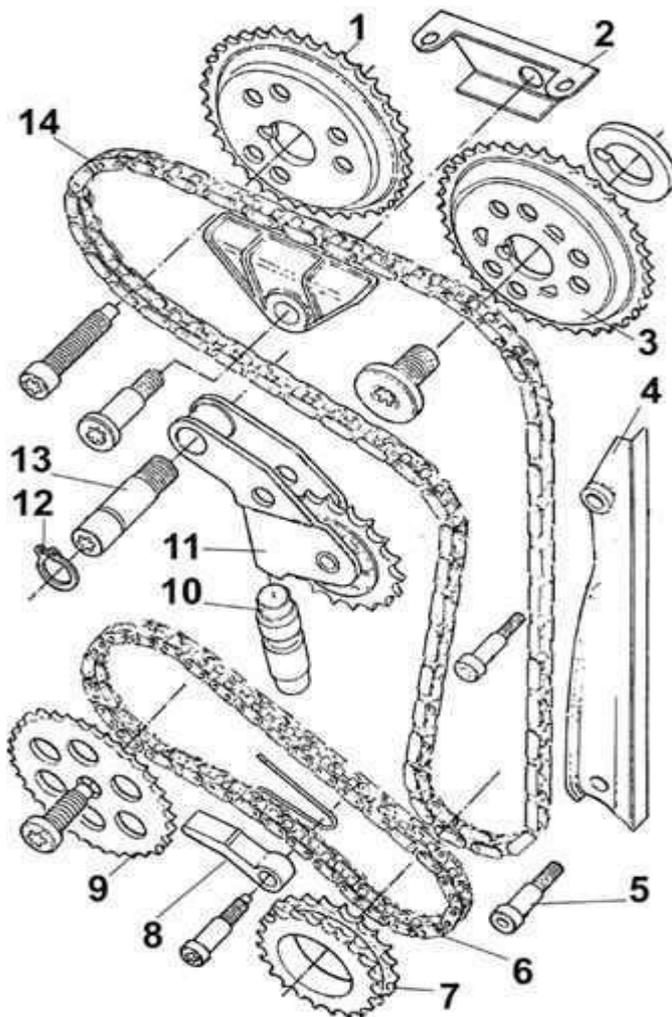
Привод ГРМ с двумя распределительными валами
